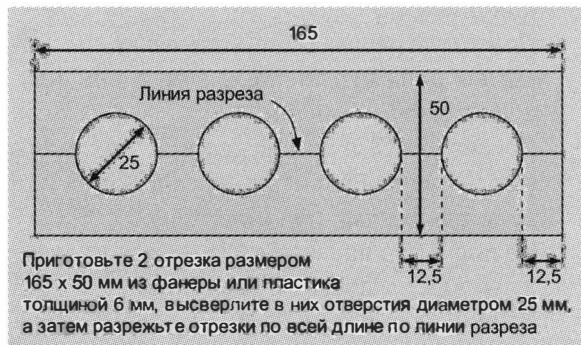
Чертежи, размеры и инструкции по изготовлению деталей монетоприемника под 16 датчиков
